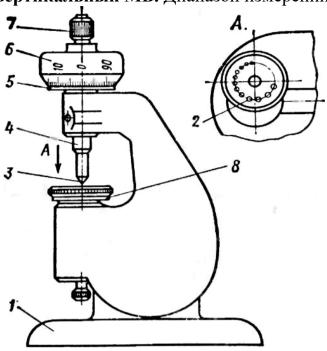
Общее устройство микрометра вертикального: 1 – корпус; 2 – поворотный диск; 3 – измерительный стержень; 5 – стебель; 6 – барабан; 7 – фрикцион; 8 – измерительный стол
